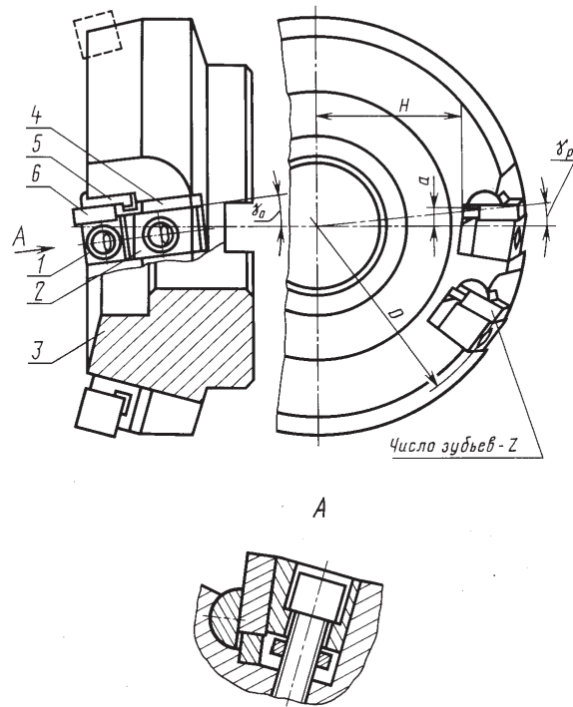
Фреза торцева з механічним кріпленням пластин ГОСТ 26595-
